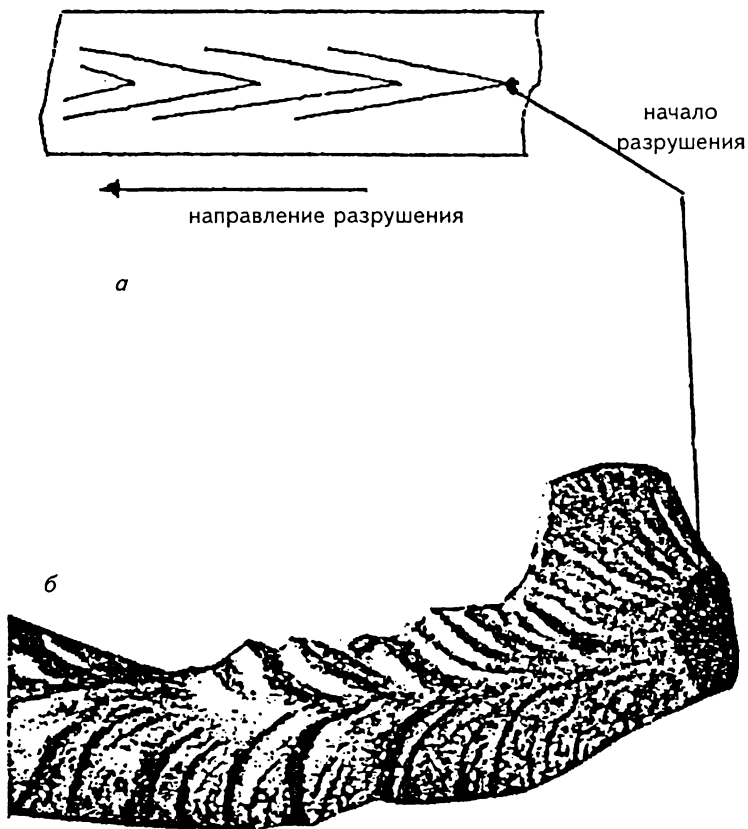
Признаки места начала разрушения: а — схема разрушения; б — шевронный излом кольца подшипника из стали ШХ15
